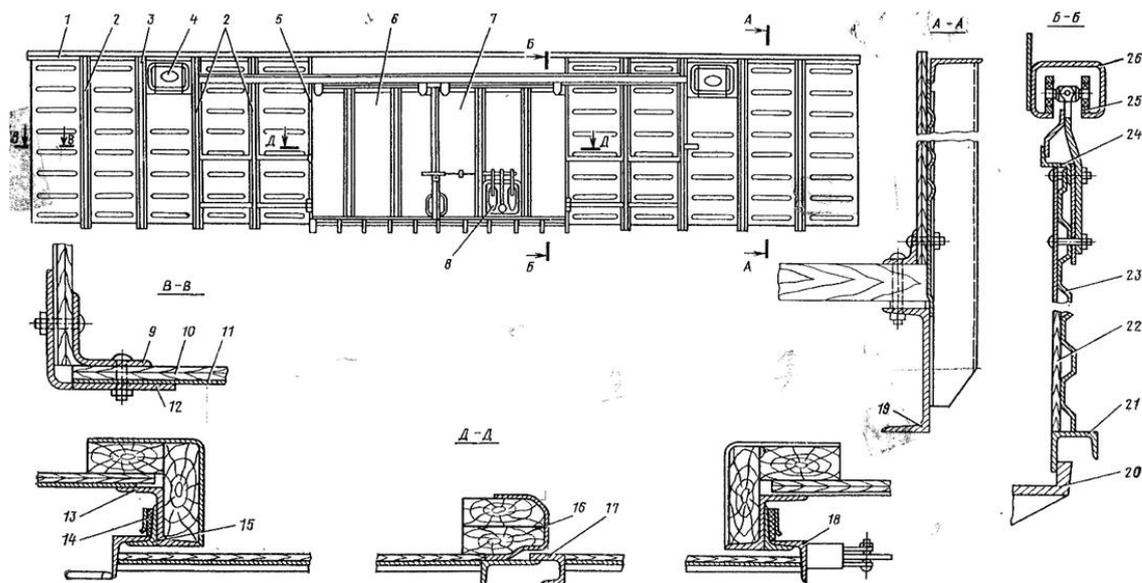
Боковая стена кузова универсального крытого вагона модели 11-217
